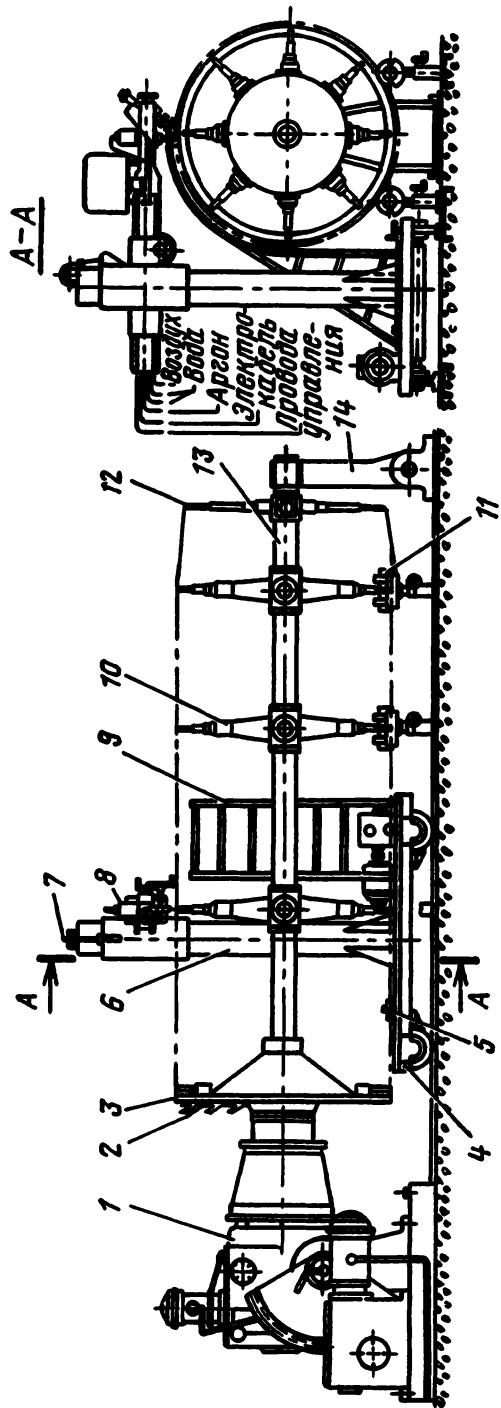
Приспособление для сварки поперечных швов металлических баков:
